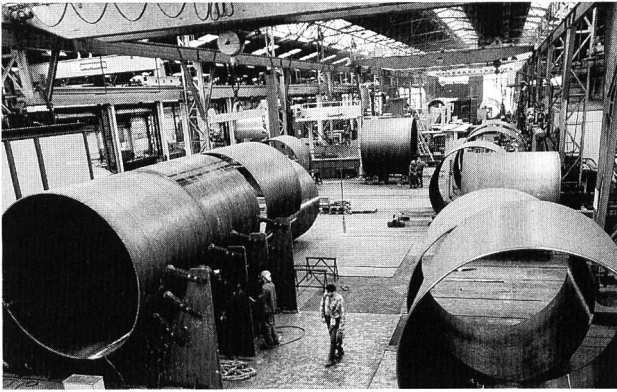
Fabrication en atelier – soudage de deux viroles.
